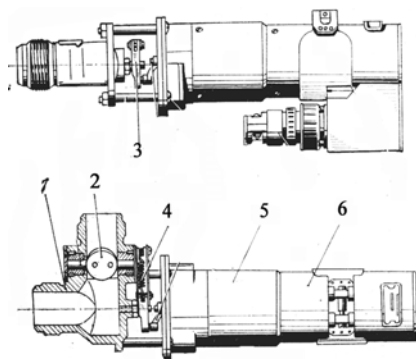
Переключатель воздуха 525А: 1 – корпус; 2 – заслонка; 3 – рычажный механизм; 4 – пружина рычажного механизма; 5 – редуктор; 6 – электродвигатель МРТ-1АТВ
